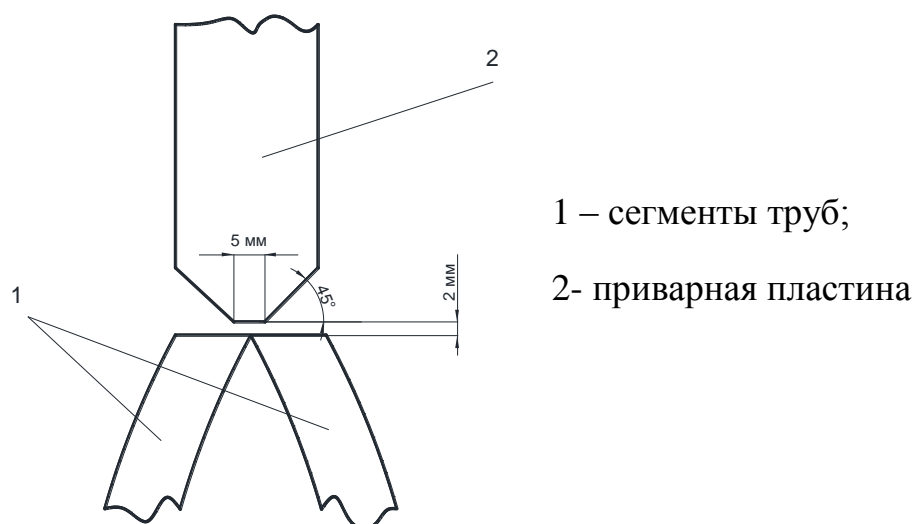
Схема подготовки кромок перед приваркой пластин
